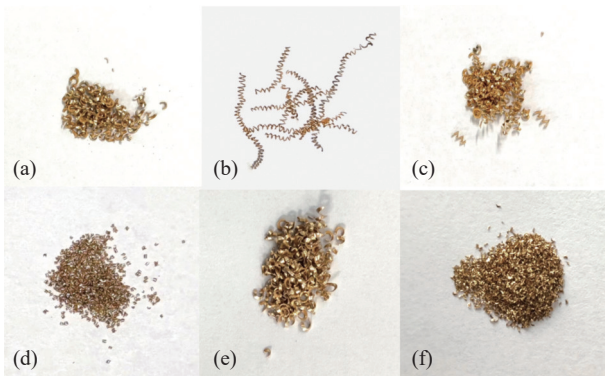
6种掺杂不同元素的黄铜合金在相同切削速度下的切屑宏观形貌: 2Sn(a); 0.5Sn(b); Sn-Fe(c); Pb(d); Si(e); H59(f)
